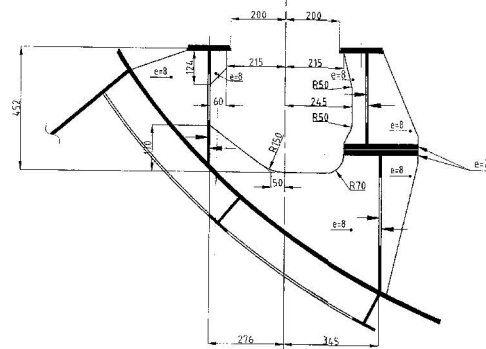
DETAIL DU PLAN DE POSE DE L'ELECTRO-POMPE
